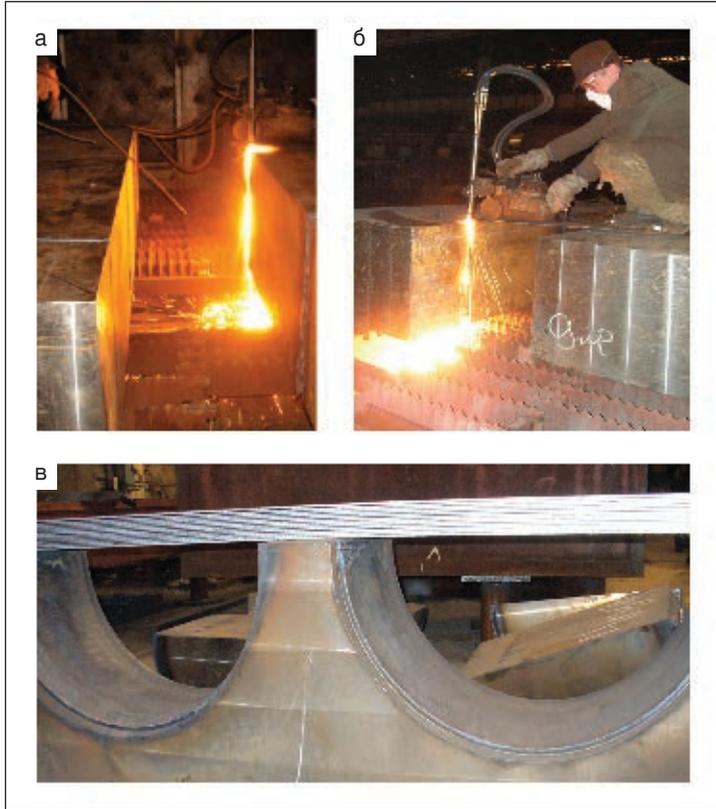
Вырезка отверстий диаметром 800 мм резакom TORH-M на заготовках корпуса подшипника толщиной 450 мм, сталь 40X: а — врезание; б — окончание резки; в — поверхность реза. Мундштук №4, диаметр режущего канала 4,5 мм
